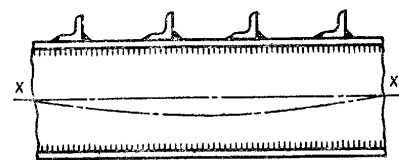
Сварная балка с несимметричным расположением поперечных швов
